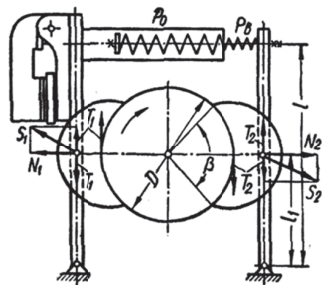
Схема механизма двухколочного тормоза с короткой кинематической цепью
